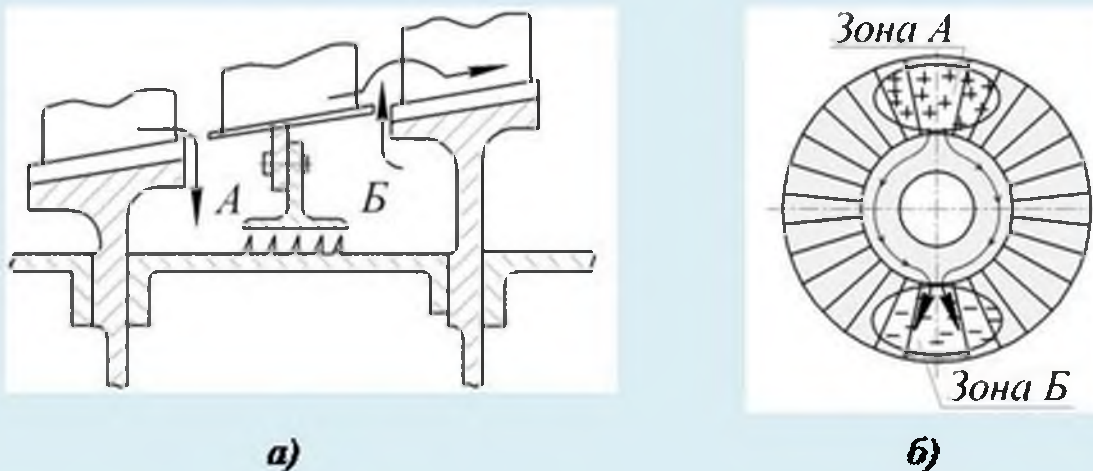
Корпус с двойной стенкой компрессора ВД ТРДД V2500:
